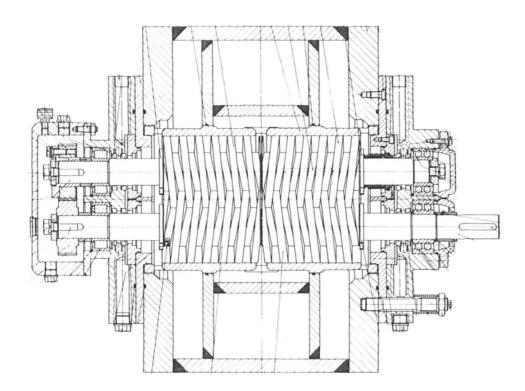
Zeichnung der von Vauth [4] eingesetzten Schraubenspindelpumpe
